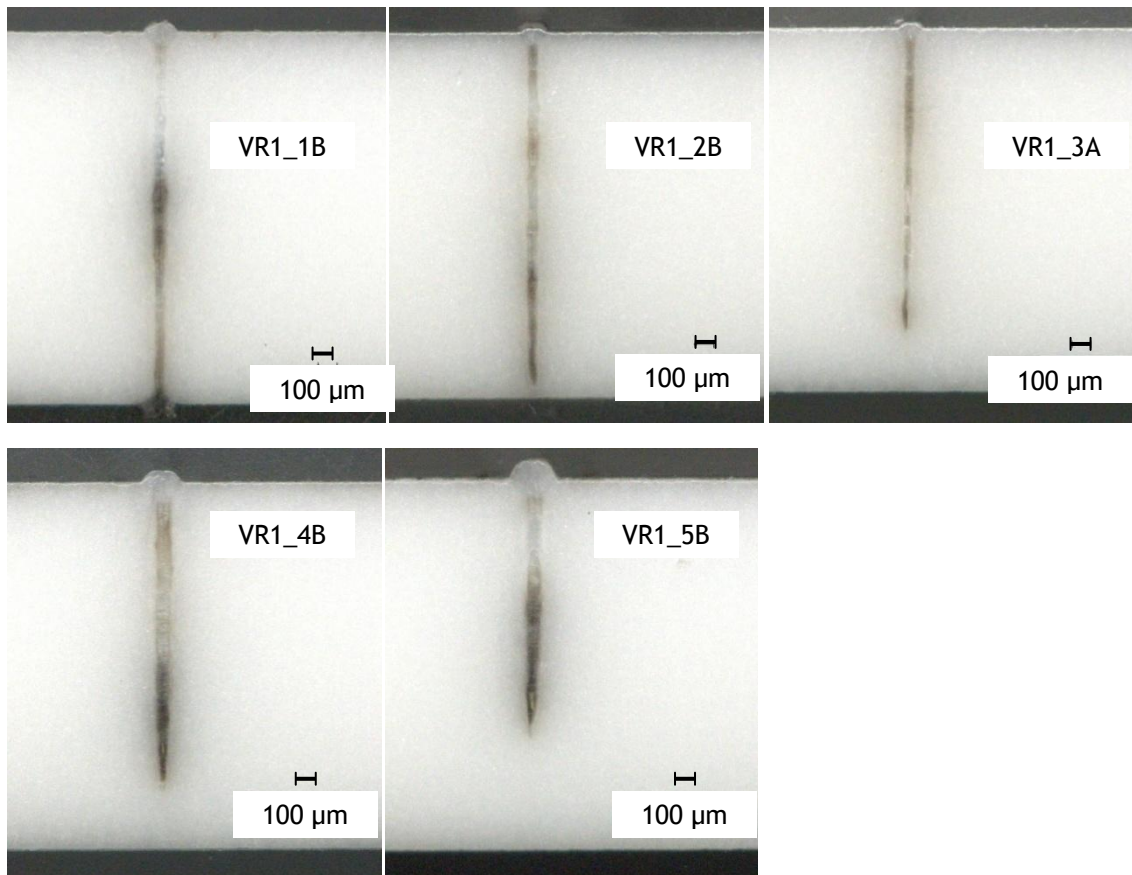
Querschliffe der Schweißnähte aus Versuchsreihe 1
